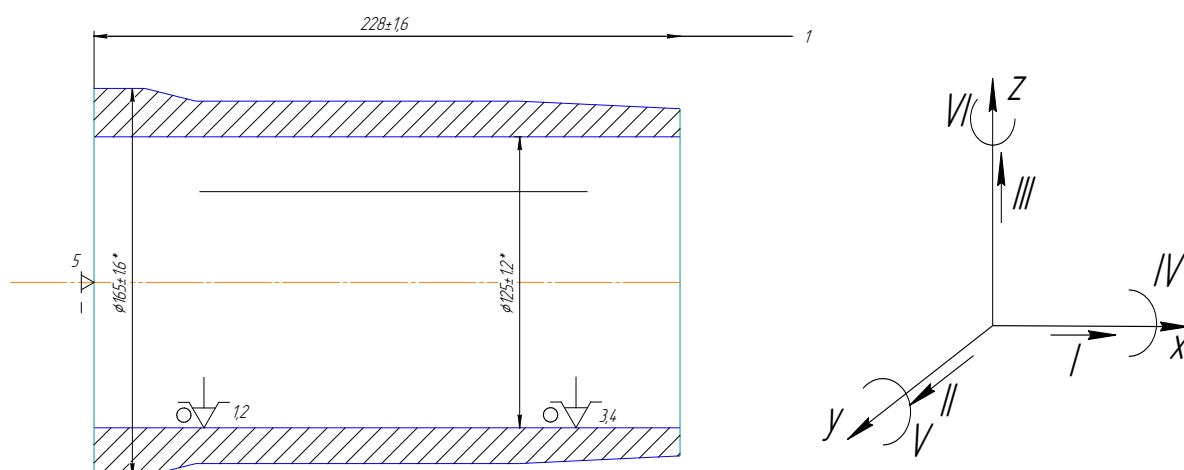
Схема базування на операції 050 токарно-гідрокопіювальна
